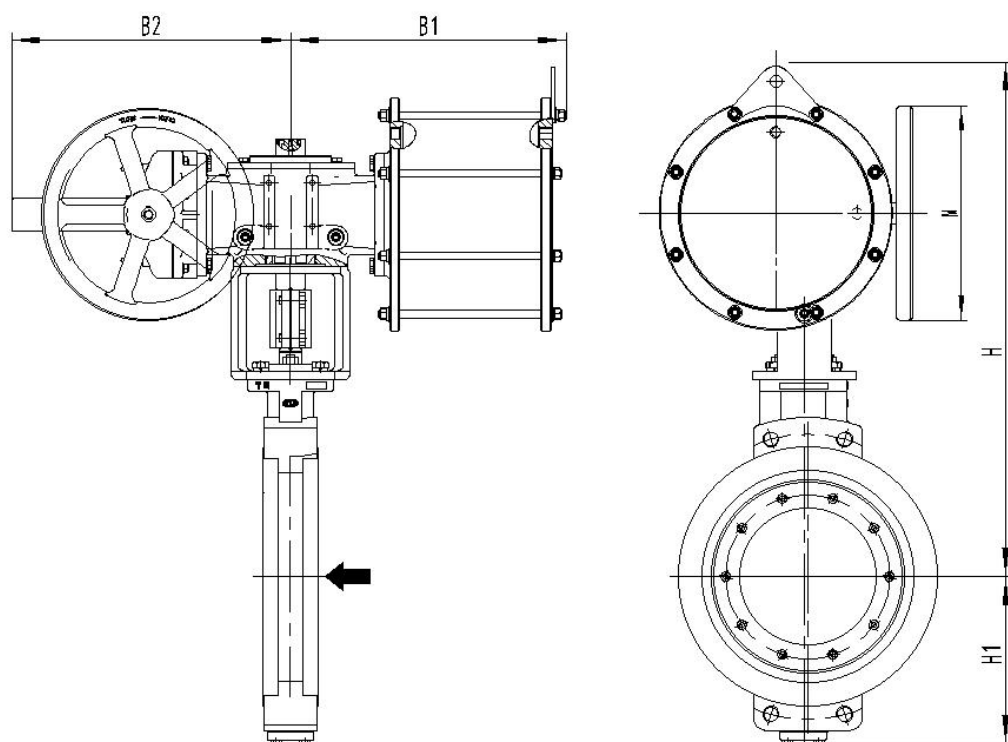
配 AW27D003~AW35D004 带伞齿手轮外形尺寸图
